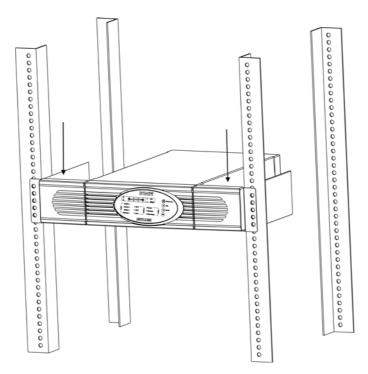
Montaggio in rack ZINTO A 800, ZINTO A 1000 - Passo 4
